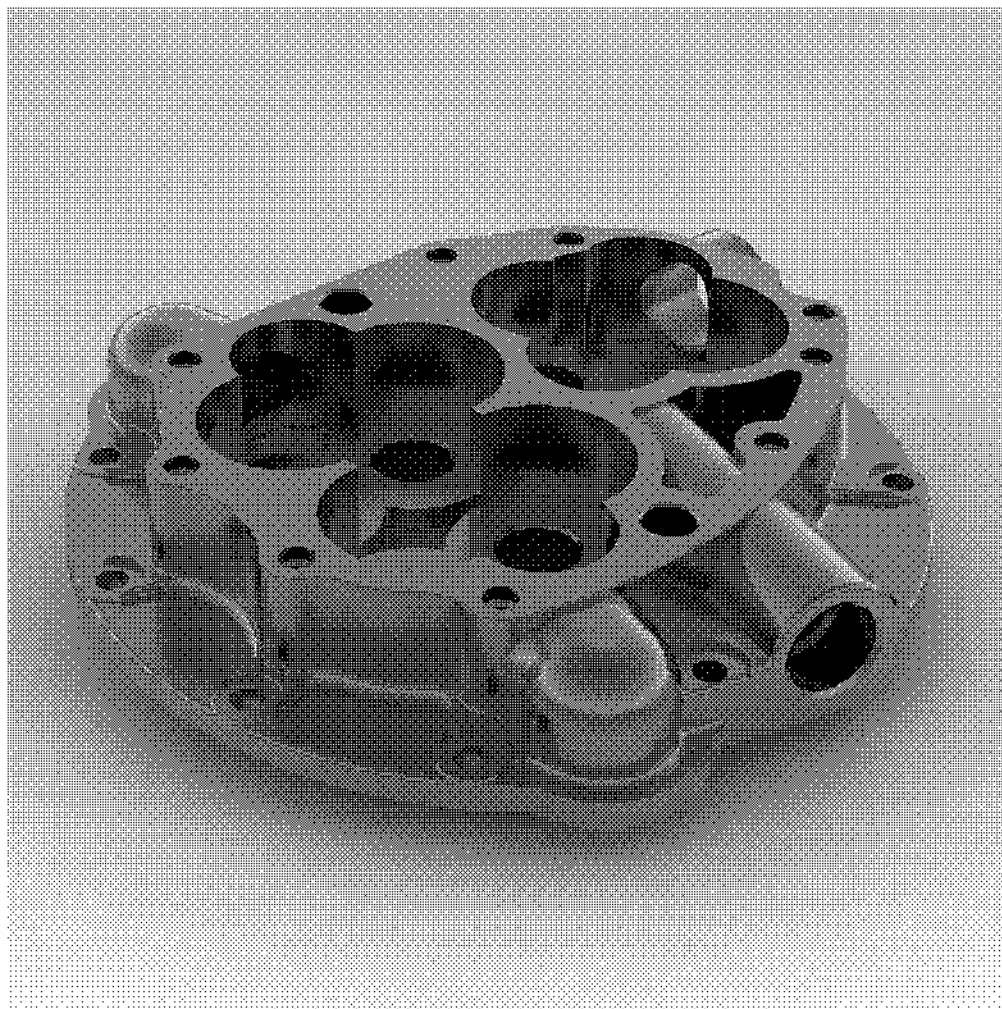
CAD модель детали «Корпус масляного насоса»
